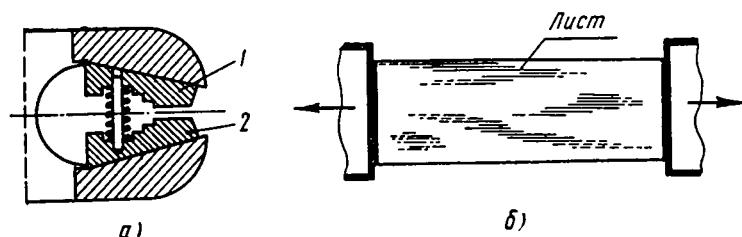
Схема головки горизонтальной правильно-растяжной машины И325 (а) и схема правки (б)
